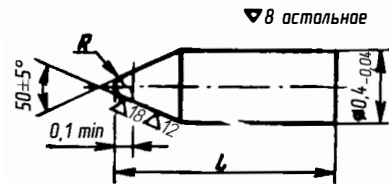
Основные размеры игл для головки звукоснимателя
